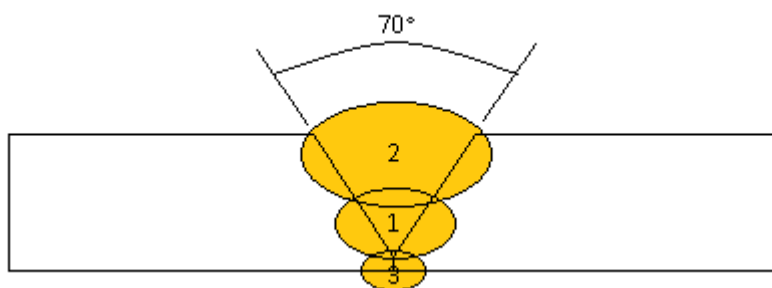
Esquema utilizado na soldagem pelo processo FCAW.
